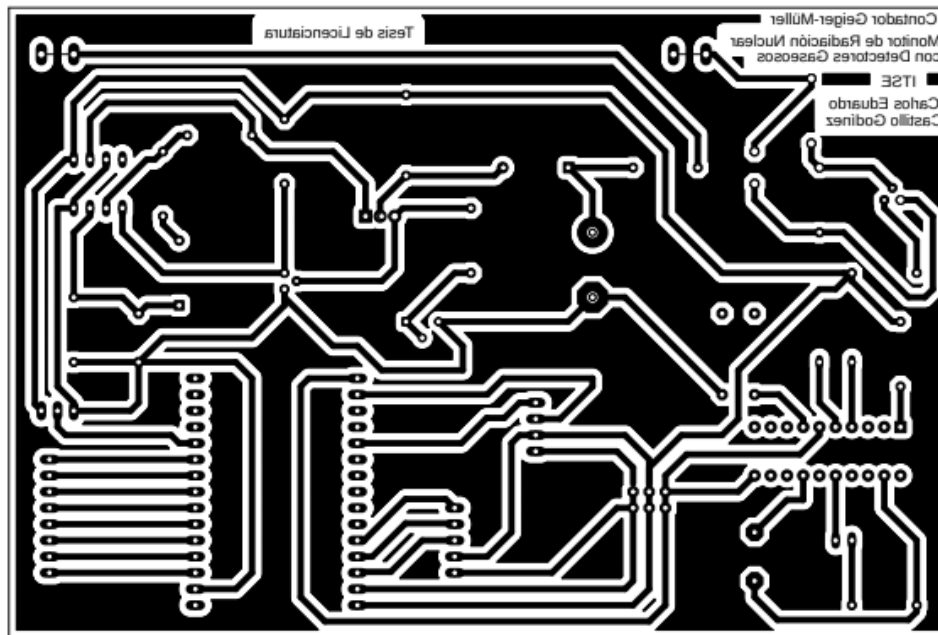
Forma final del diseño PCB utilizado en la tesis.
